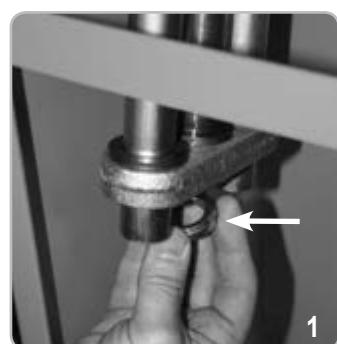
Insérer le ressort qui vient d'être assemblé sur le tube central.
